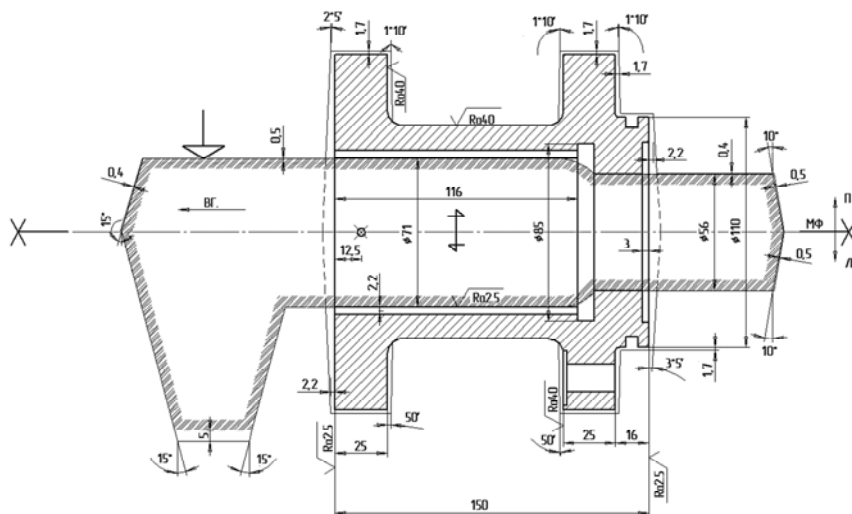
Чертеж детали «Корпус» с литейно-модельными указаниями
